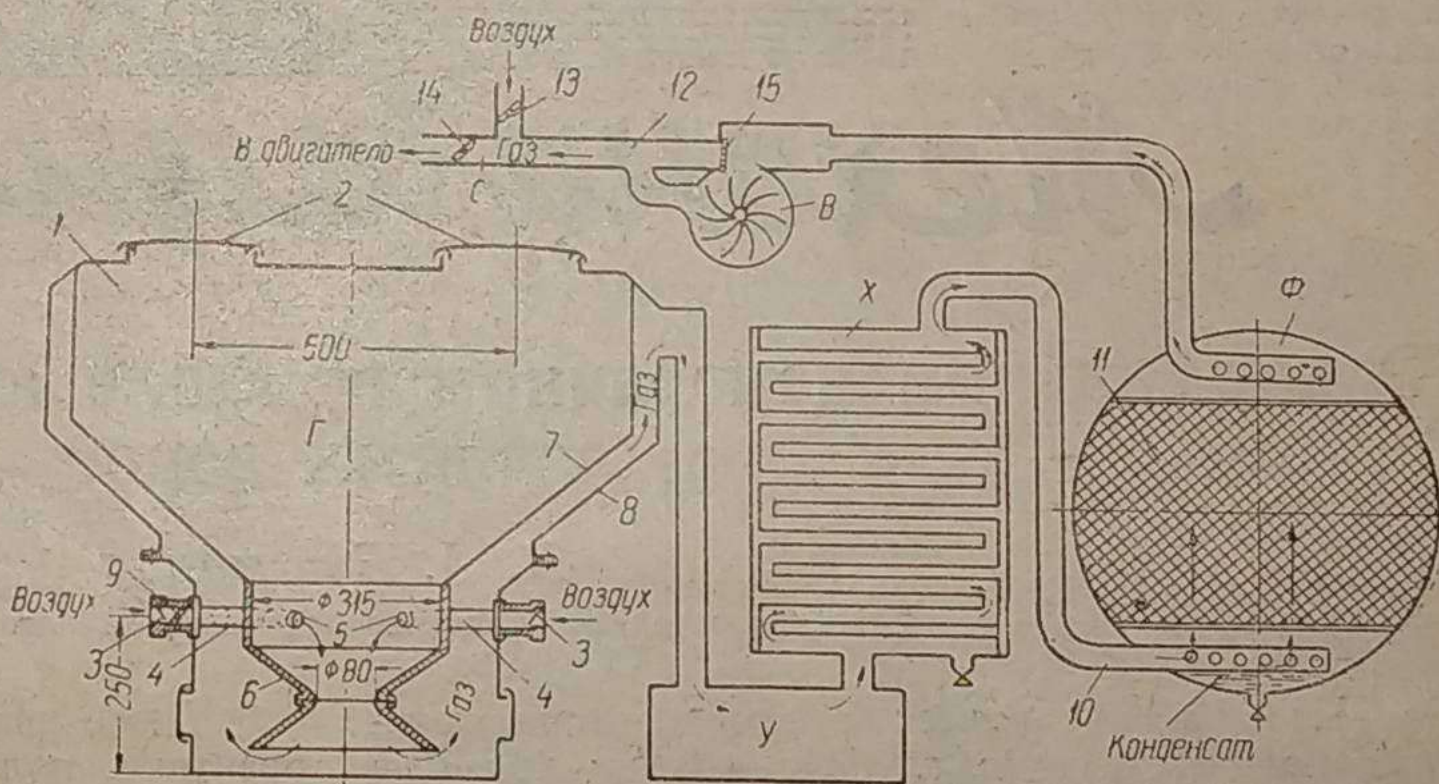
Схема газогенераторной установки Пельцера для автомобиля М-1
